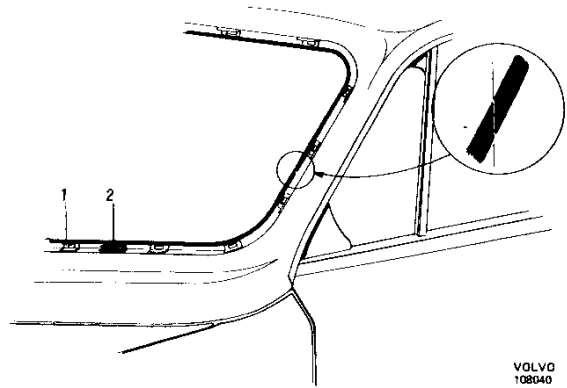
Fugenschnitt für Butylklebeband sowie Anbringung der Abstandklötze
